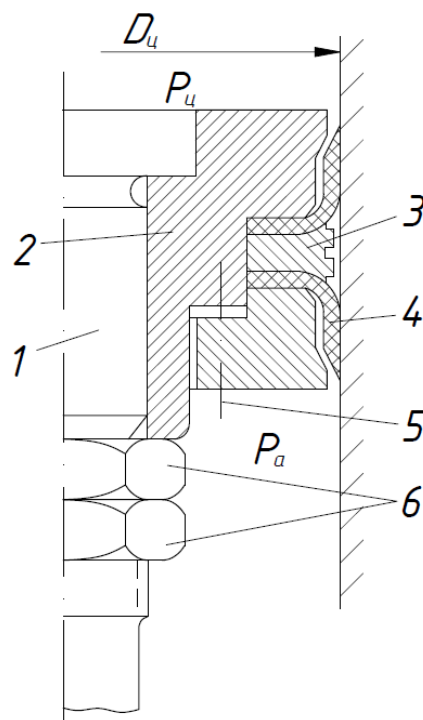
Уплотнение поршня манжетами: 1 – шток; 2 – поршень; 3 – прижимное кольцо; 4 – манжета; 5 – шпилька; 6 – гайка и контргайка с двумя манжетами [8]
